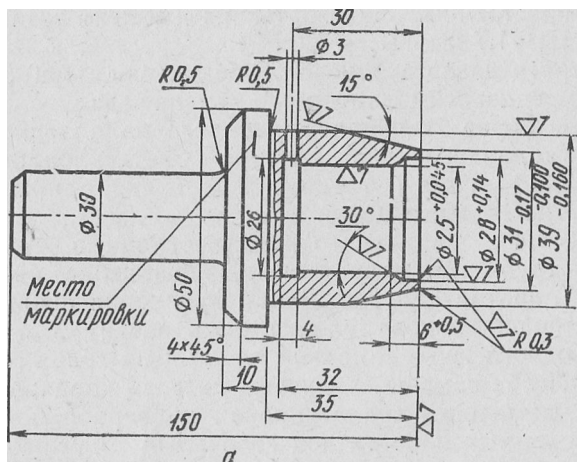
Оправки для напрессовки торцового уплотнения на шипы крестовин валов привода мостов:
